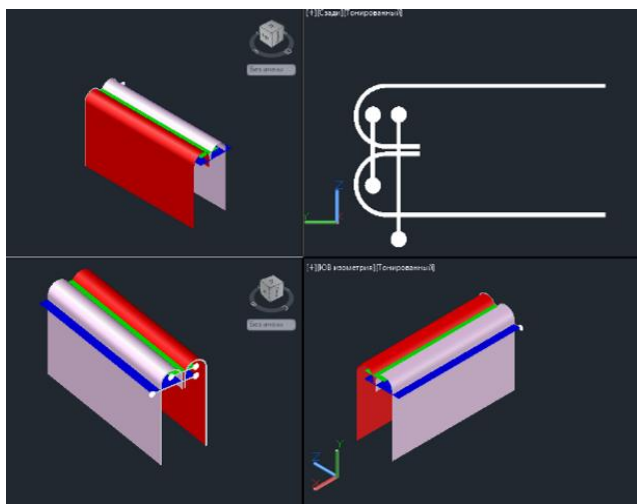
3D-модель складальної схеми обробки вузла
